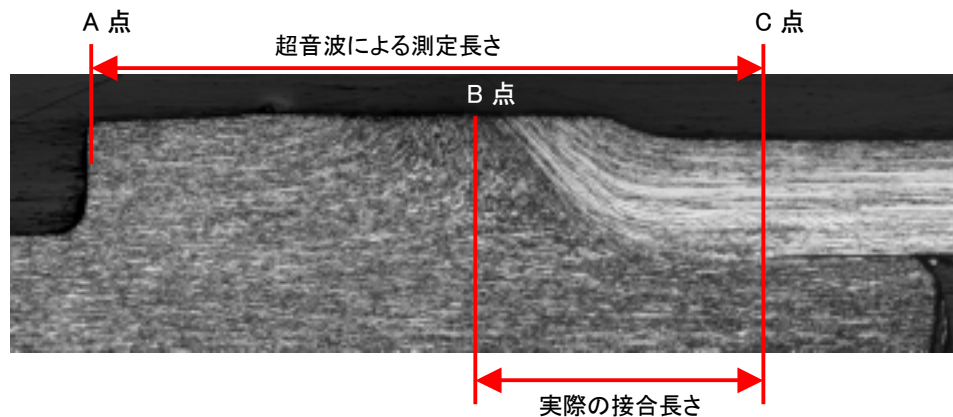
抵抗溶接部の実際の接合長さと超音波による測定位置
